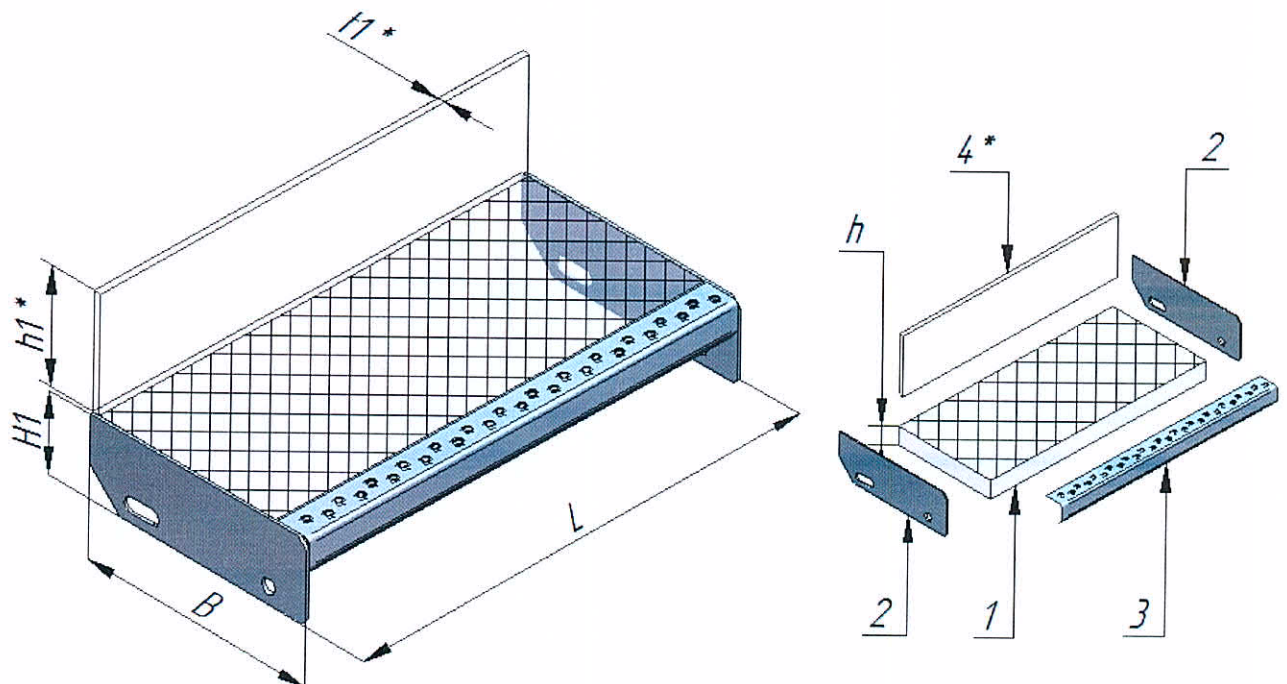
Ступень металлическая основные размеры и конструктивные элементы.
